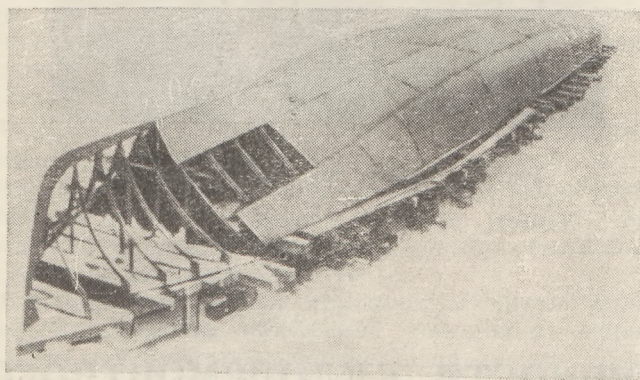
Корпус пассажирского теплохода типа М-21 мощностью 150 л. с. в процессе сварки обшивки
